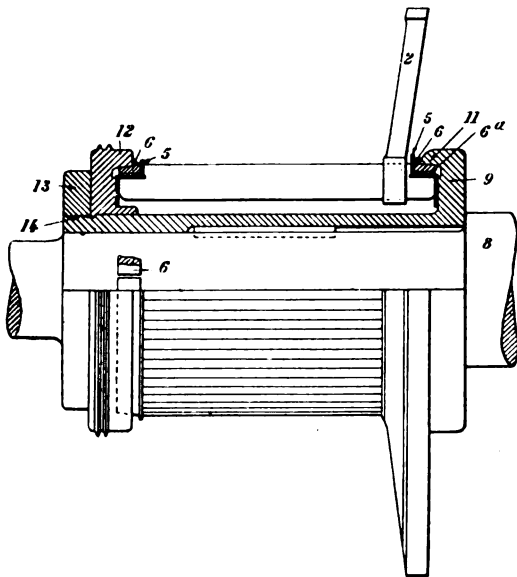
Coupe par l'axe et vue d'un collecteur Jackson et Lewis.
